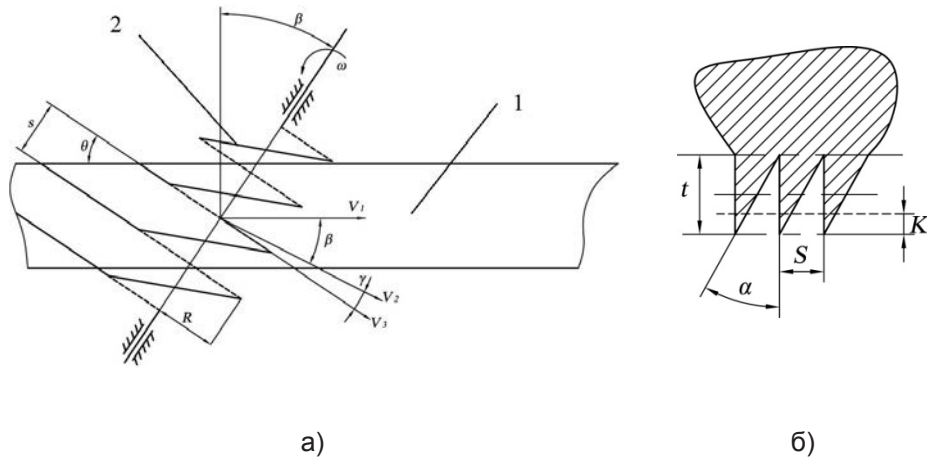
Принципова схема пристрою та розріз гвинтового ножа
